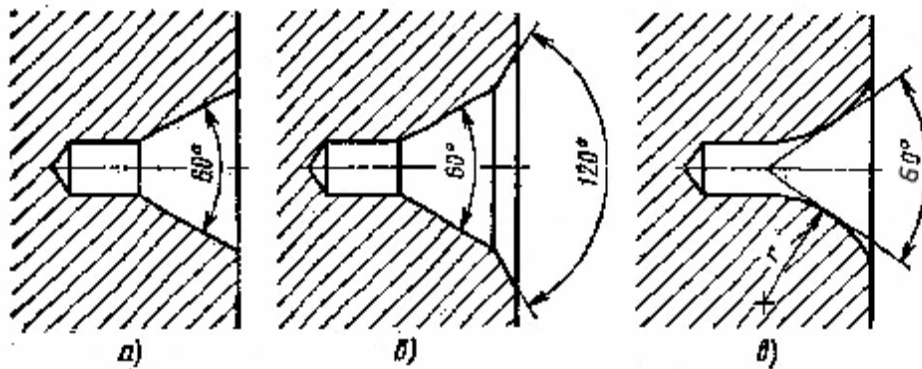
Виды центровых отверстий: а) без предохранительного конуса, б) с предохранительным конусом, в) с дугообразной образующей
